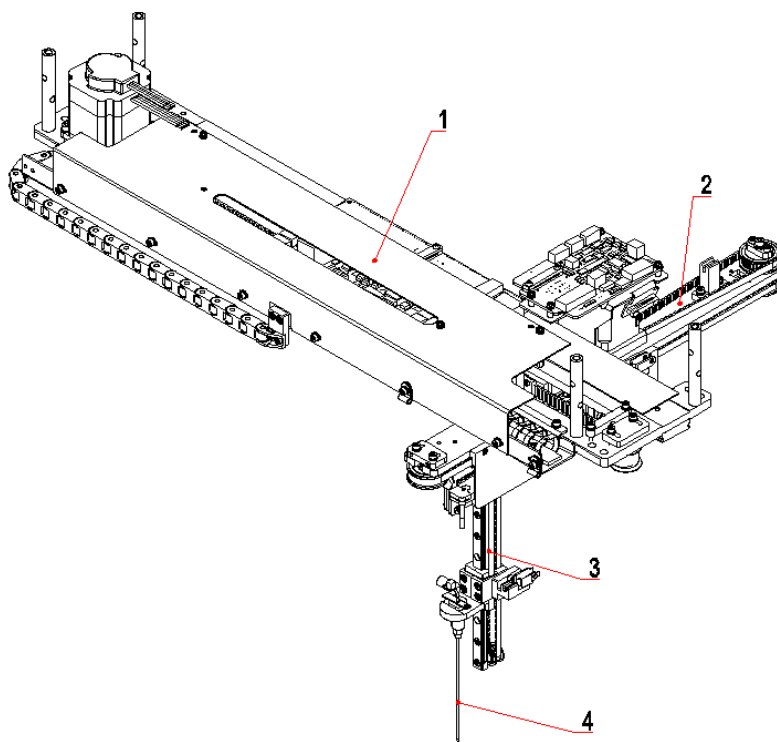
Схематический чертеж держателя левого дозатора реагентов
